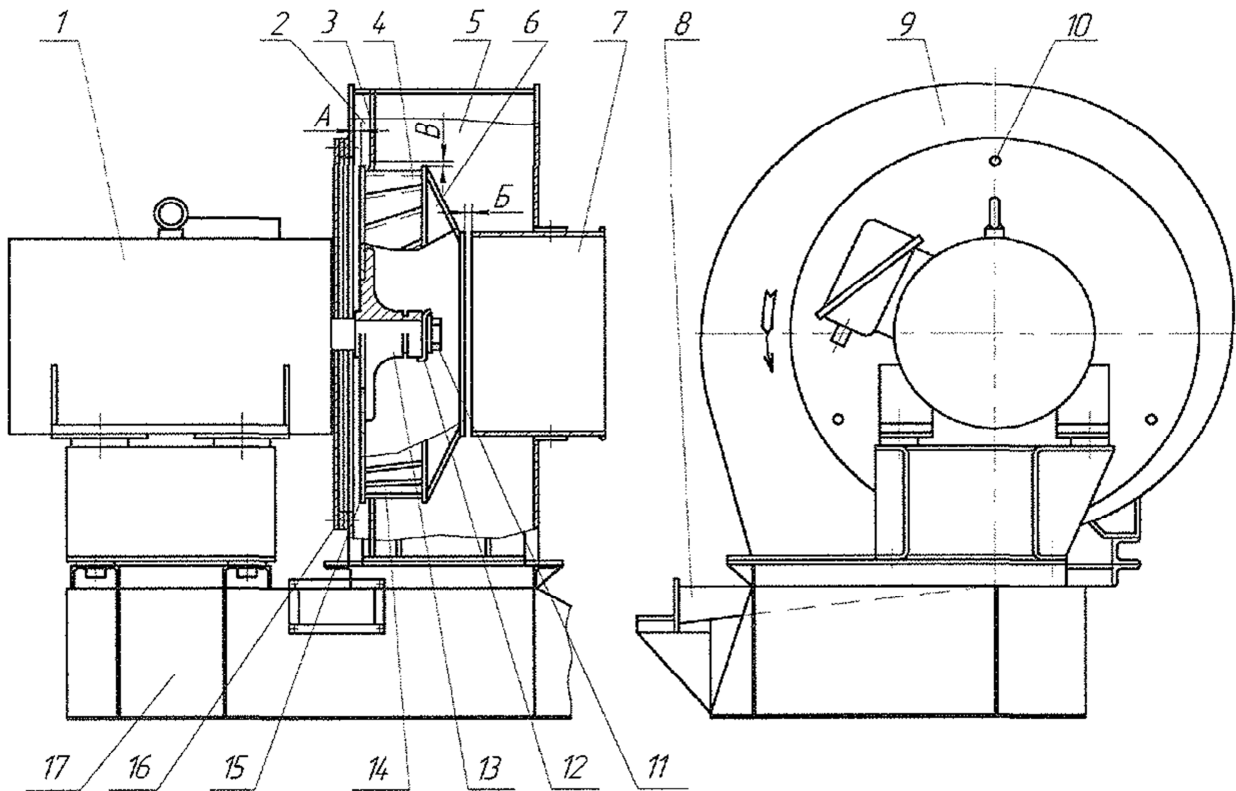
Блок центробежного вентилятора-воздухоочистителя ЦВ9-37,6-7,6
